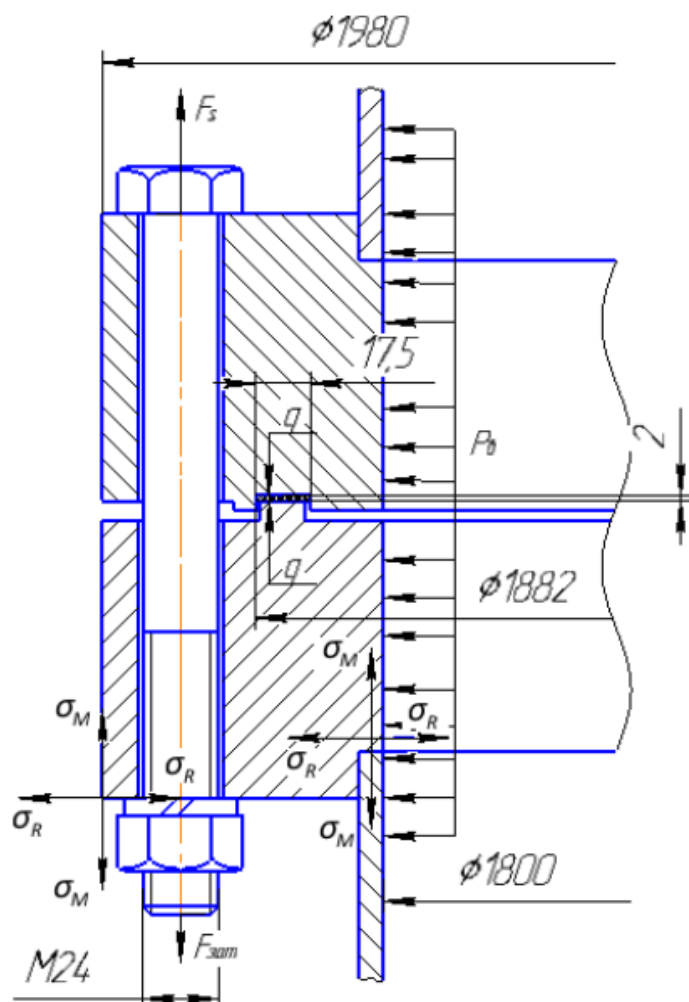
Расчётная схема фланцевого соединения крышки с корпусом
